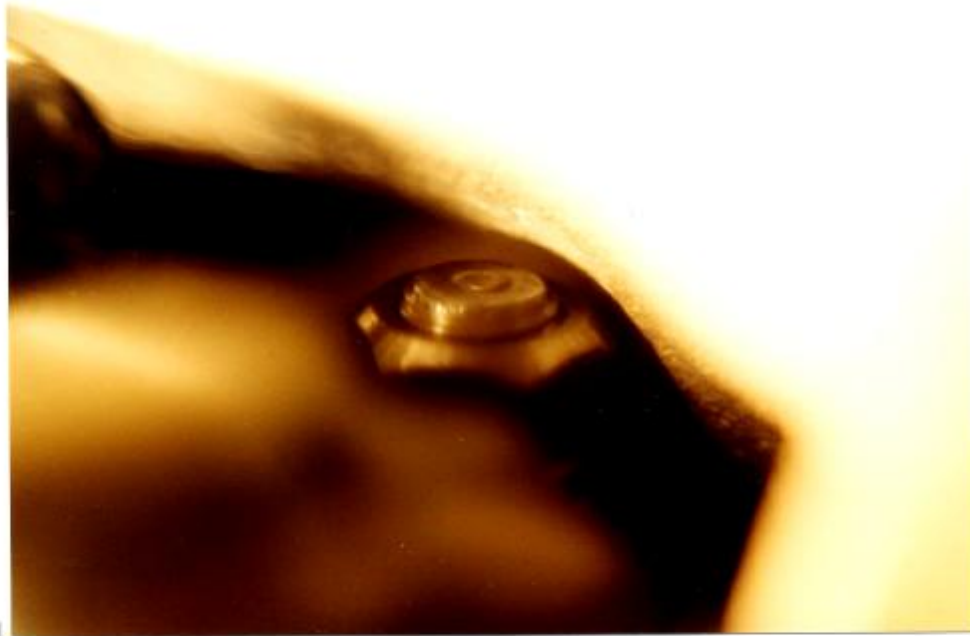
Blockausfräsungen und angepflaste Pleuelschrauben-Mutter, um auch hier (Pleuelschrauben-Mutter zu Motorblock) das min. Spaltmaß sicherzustellen.
